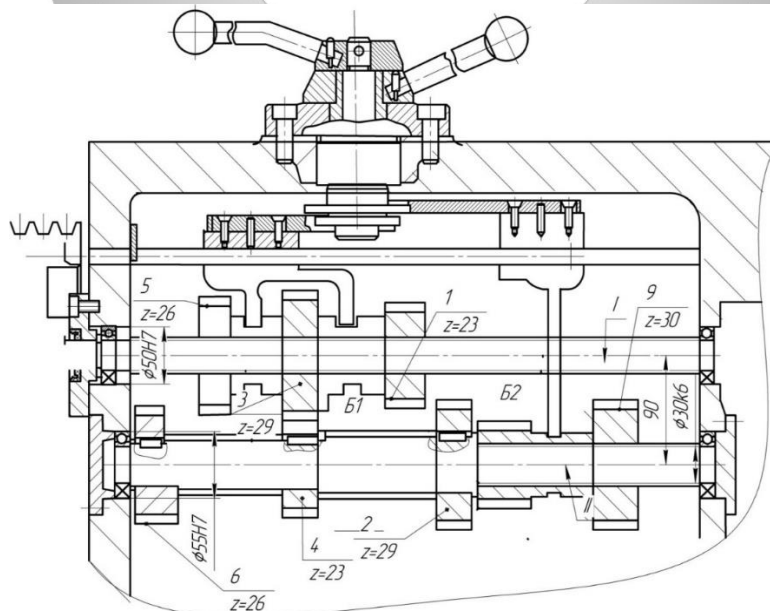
Конструктивна схема механізму перемикання блоків коробки на 1 і 2 валах.
